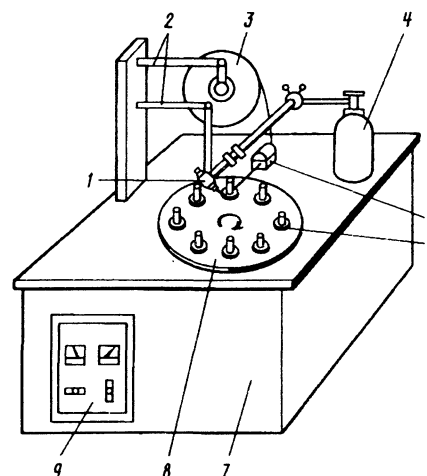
Установка для дуговой сваркопайки с присадкой припоя
